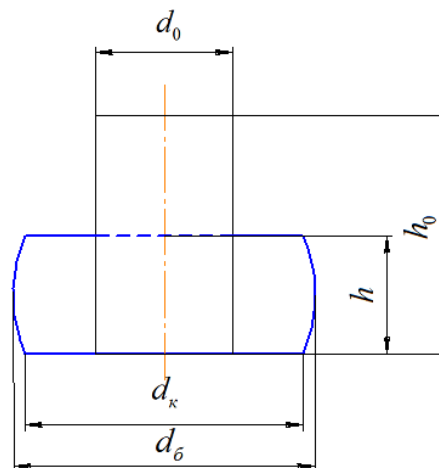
Параметры формоизменения цилиндрической заготовки в процессе осадки
